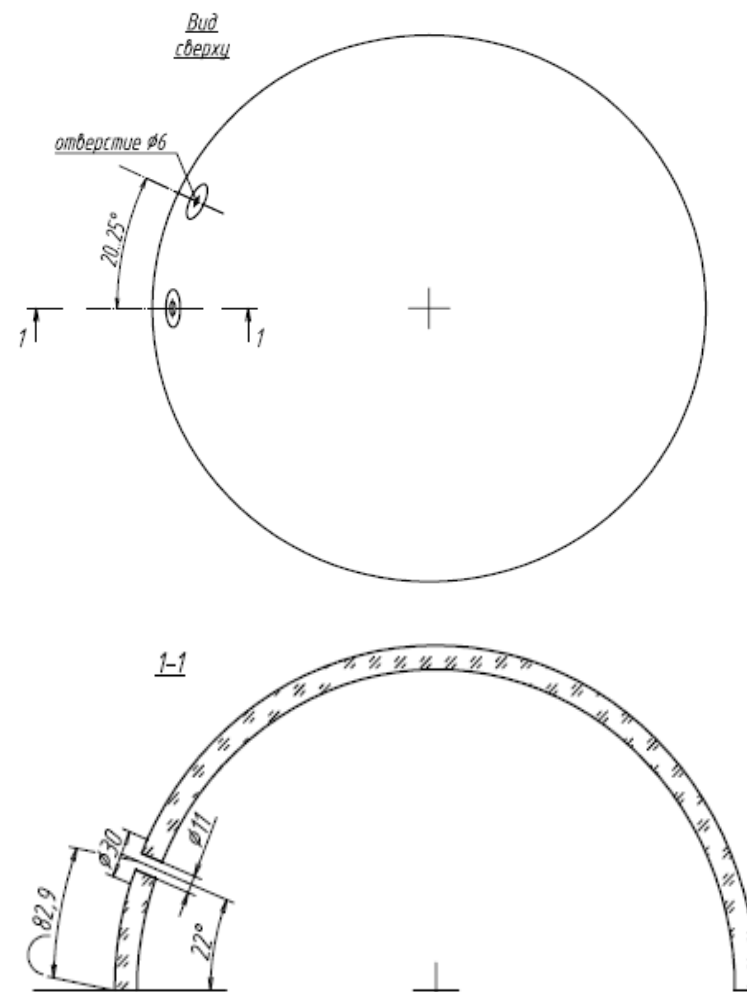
чертеж глубоководного корпуса ОМ
